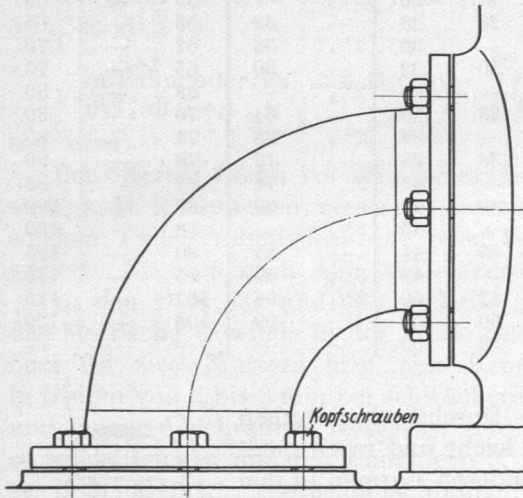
Krümmerbefestigung mit Stift- und Kopfschrauben.
